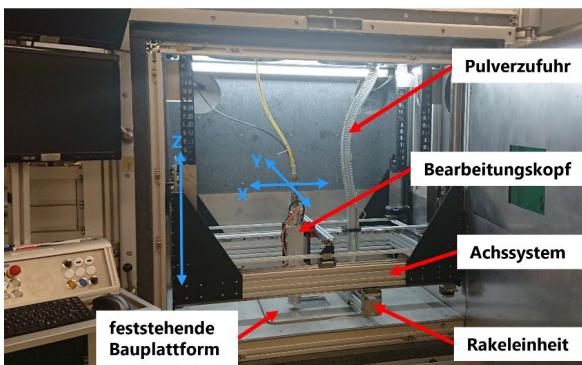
Erste Prototypen-Anlage für das Makro-SLM.
